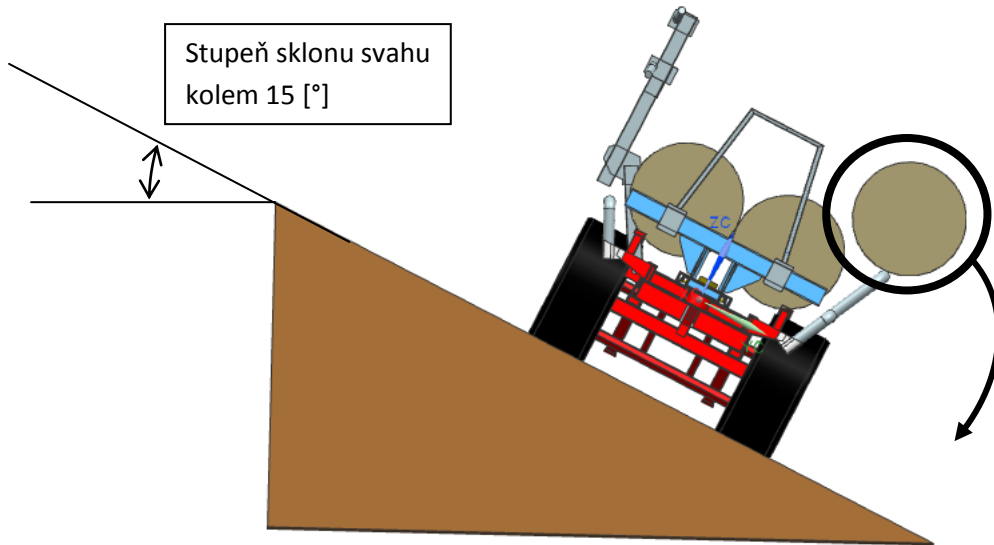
Základní pohled na 3D CAD model a popis částí - 2
